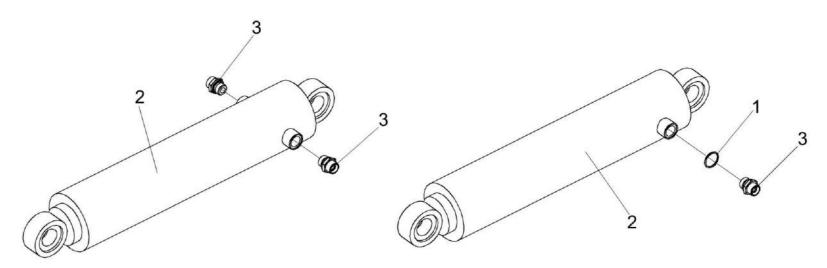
Гидроцилиндры навески КВК 0602500Б и КВК 0602500Б-01
